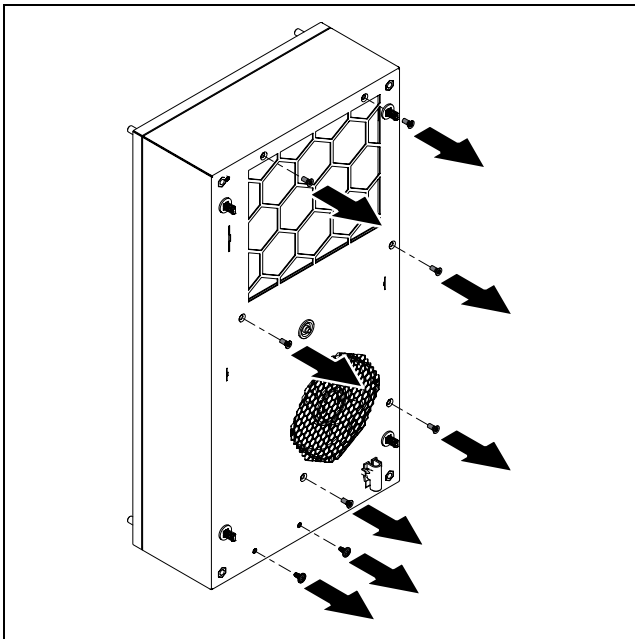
Lösen der Befestigungsschrauben (für SK 347880x, SK 347980x und SK 3480800)
